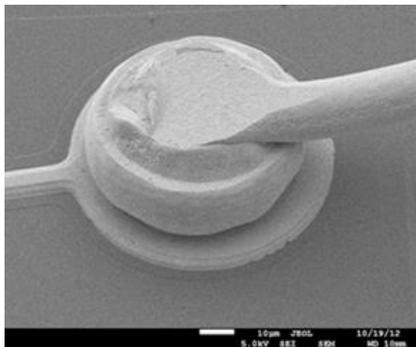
Фото сварного соединения клин на шарике
